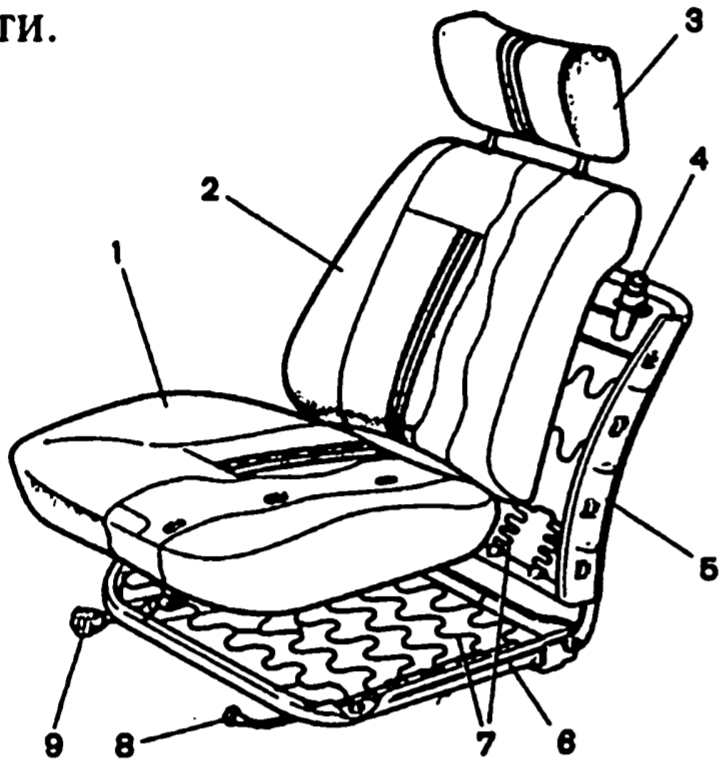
Переднее сиденье: 1 - подушка; 2 - спинка; 3 - подголовник; 4 - направляющая подголовника; 5 - каркас спинки; 6 - каркас подушки; 7 - пружины; 8 - рукоятка механизма передвижения; 9 - рукоятка механизма наклона спинки
